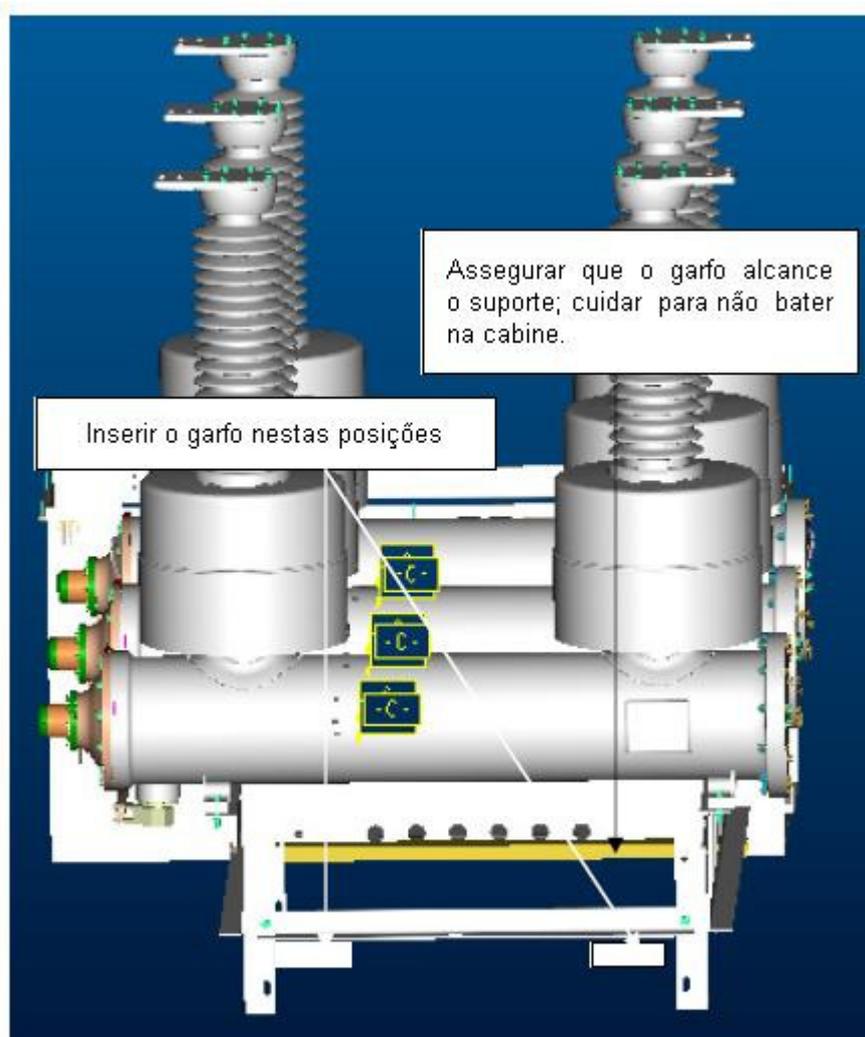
Elevação com Empilhadeira para Remessas em Contêiner
